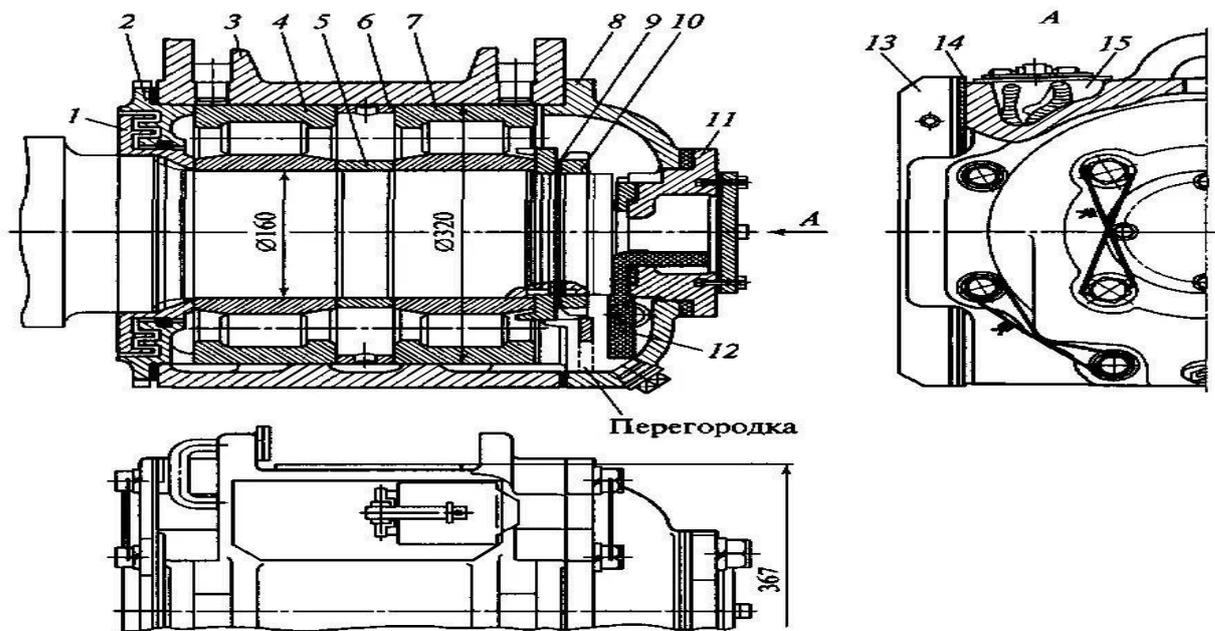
Челюстная букса тепловоза: 1 - лабиринтное уплотнение; 2 - задняя крышка; 3 - корпус; 4, 7- роликовые подшипники; 5, 6 - дистанционные кольца; 8 - передняя крышка; 9 - шайба; 10 - гайка; 11 - осевой упор; 12 - фитиль; 13 - упорный бурт; 14 - боковой наличник; 15 – масленка
